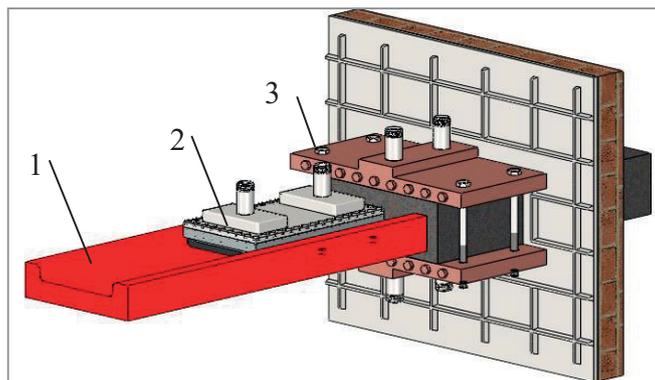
Положение формы в процессе литья: 1 – отливка; 2 – форма; 3 – кристаллизатор (элементы крепления и трубопроводы не показаны)
